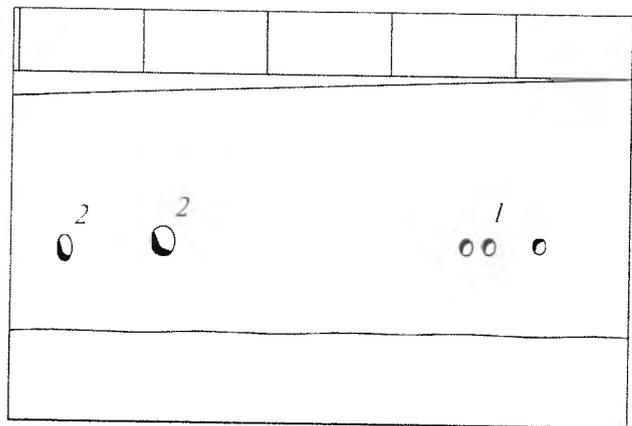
Цепочка пор – группа пор в сварном шве, расположенных в линию, в угловом сварном соединении штуцера с трубопроводом
